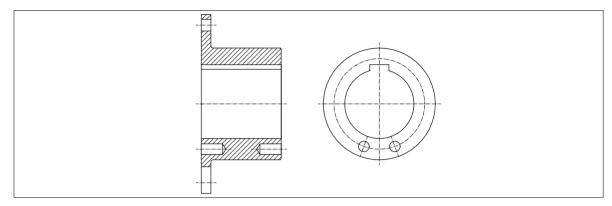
Disposición del taladro de compensación en el equilibrado en un plano
